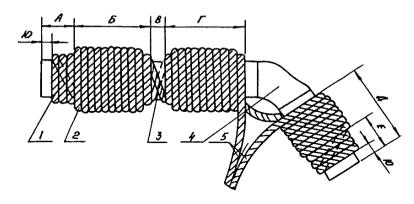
Схема намотки ДШ на корпус плейфого зажима.
